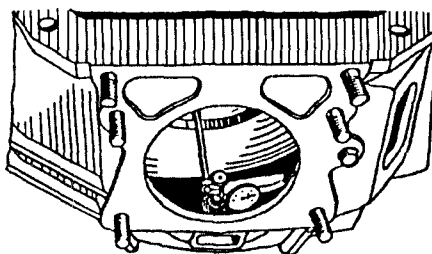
Проверка concentричности отверстия картера сцепления с осью коленчатого вала приспособлением 24-У-114525
